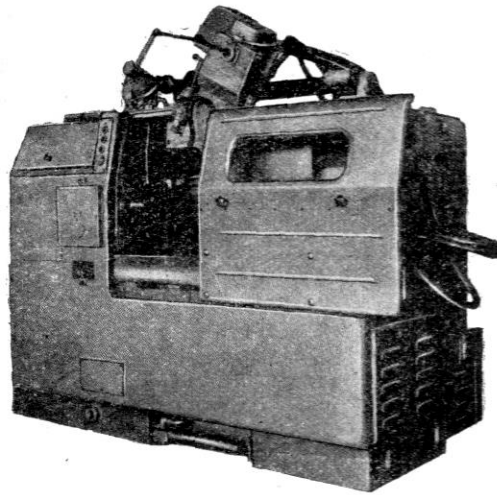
Токарно – копіювальний багаторізцевий напівавтомат модель 1708
